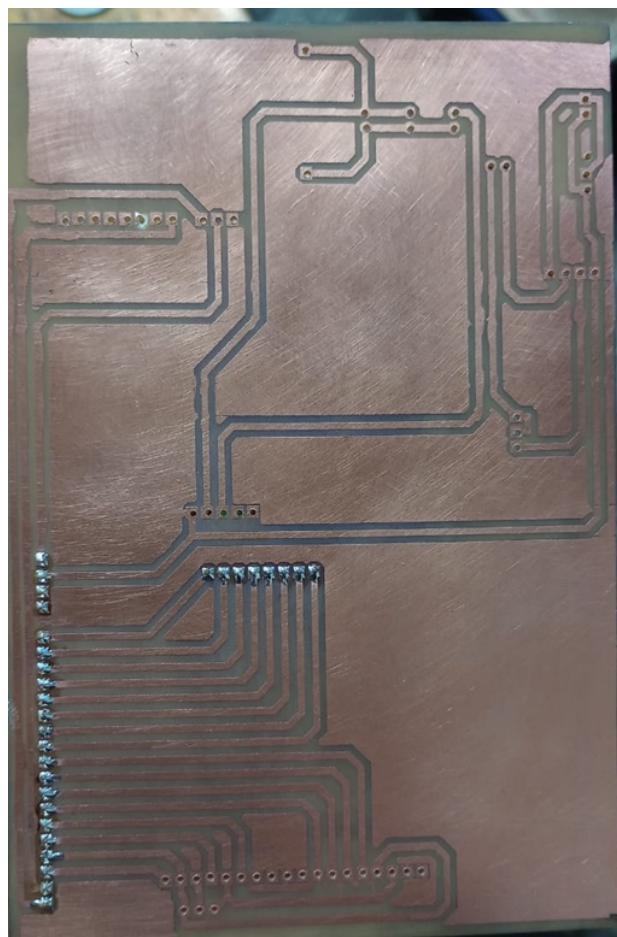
Proceso de soldadura. Fuente: Elaboración propia
